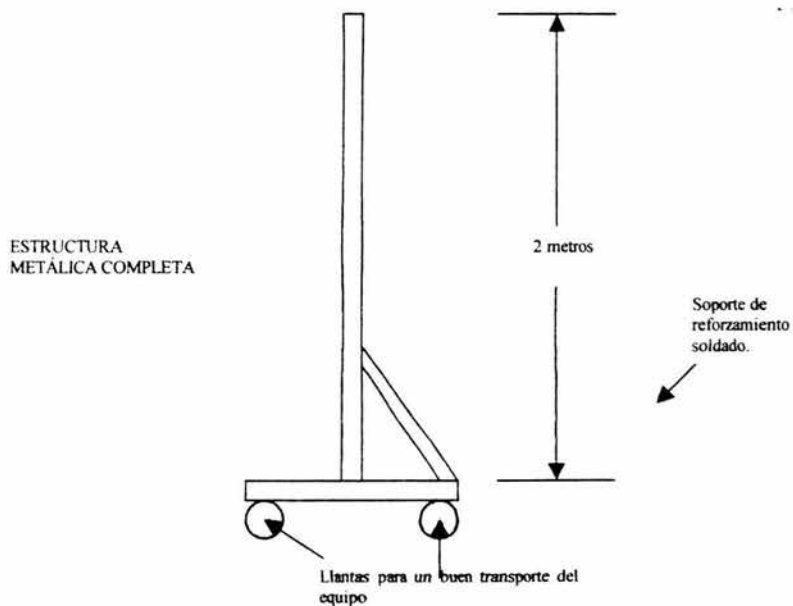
Soporte horizontal y vertical ensamblados(visto de perfil).
